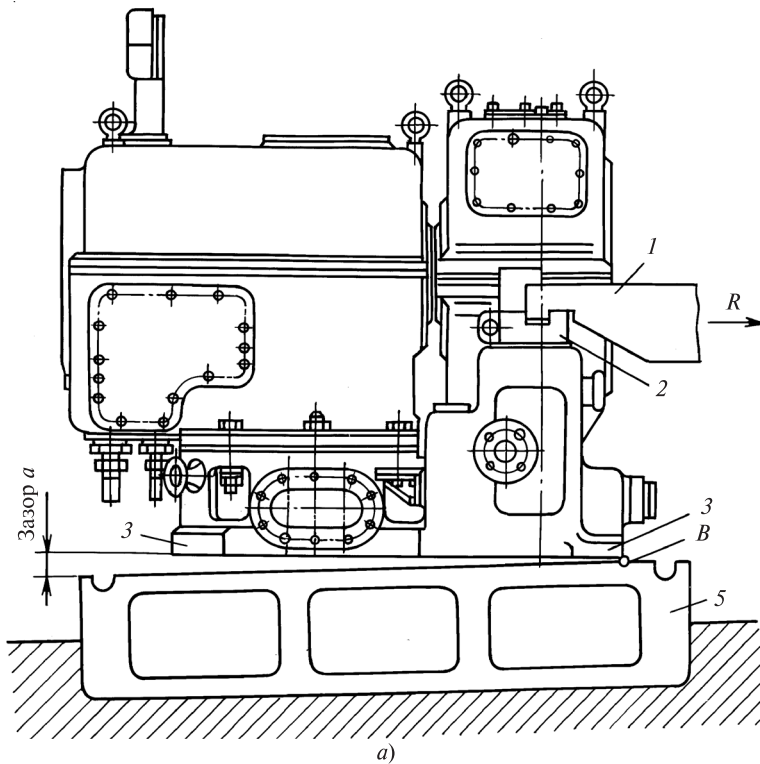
Крепление корпуса подшипника к фундаментной раме
